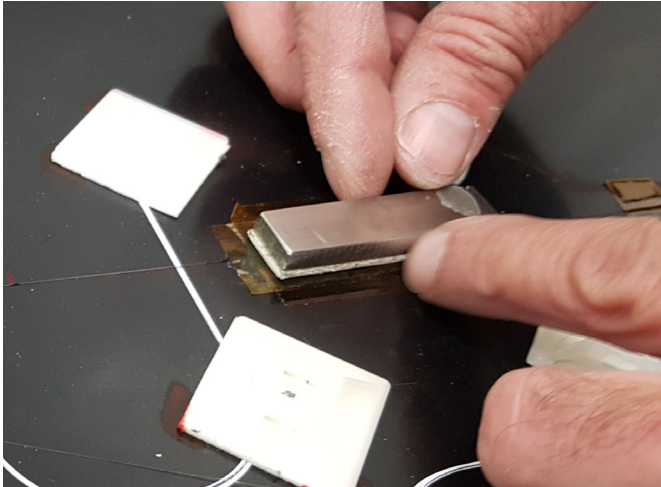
Ausrichten von Gummi und steifem Hilfswerkzeug
